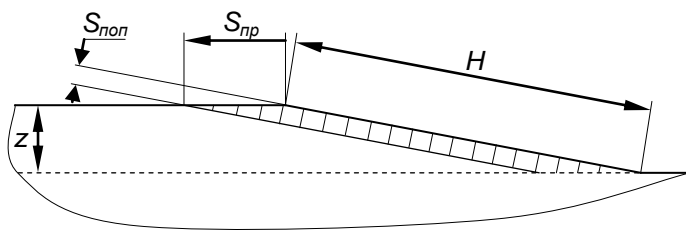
Схема съема припуска при бесцентровом шлифовании со скрещивающимися осями инструмента и детали
